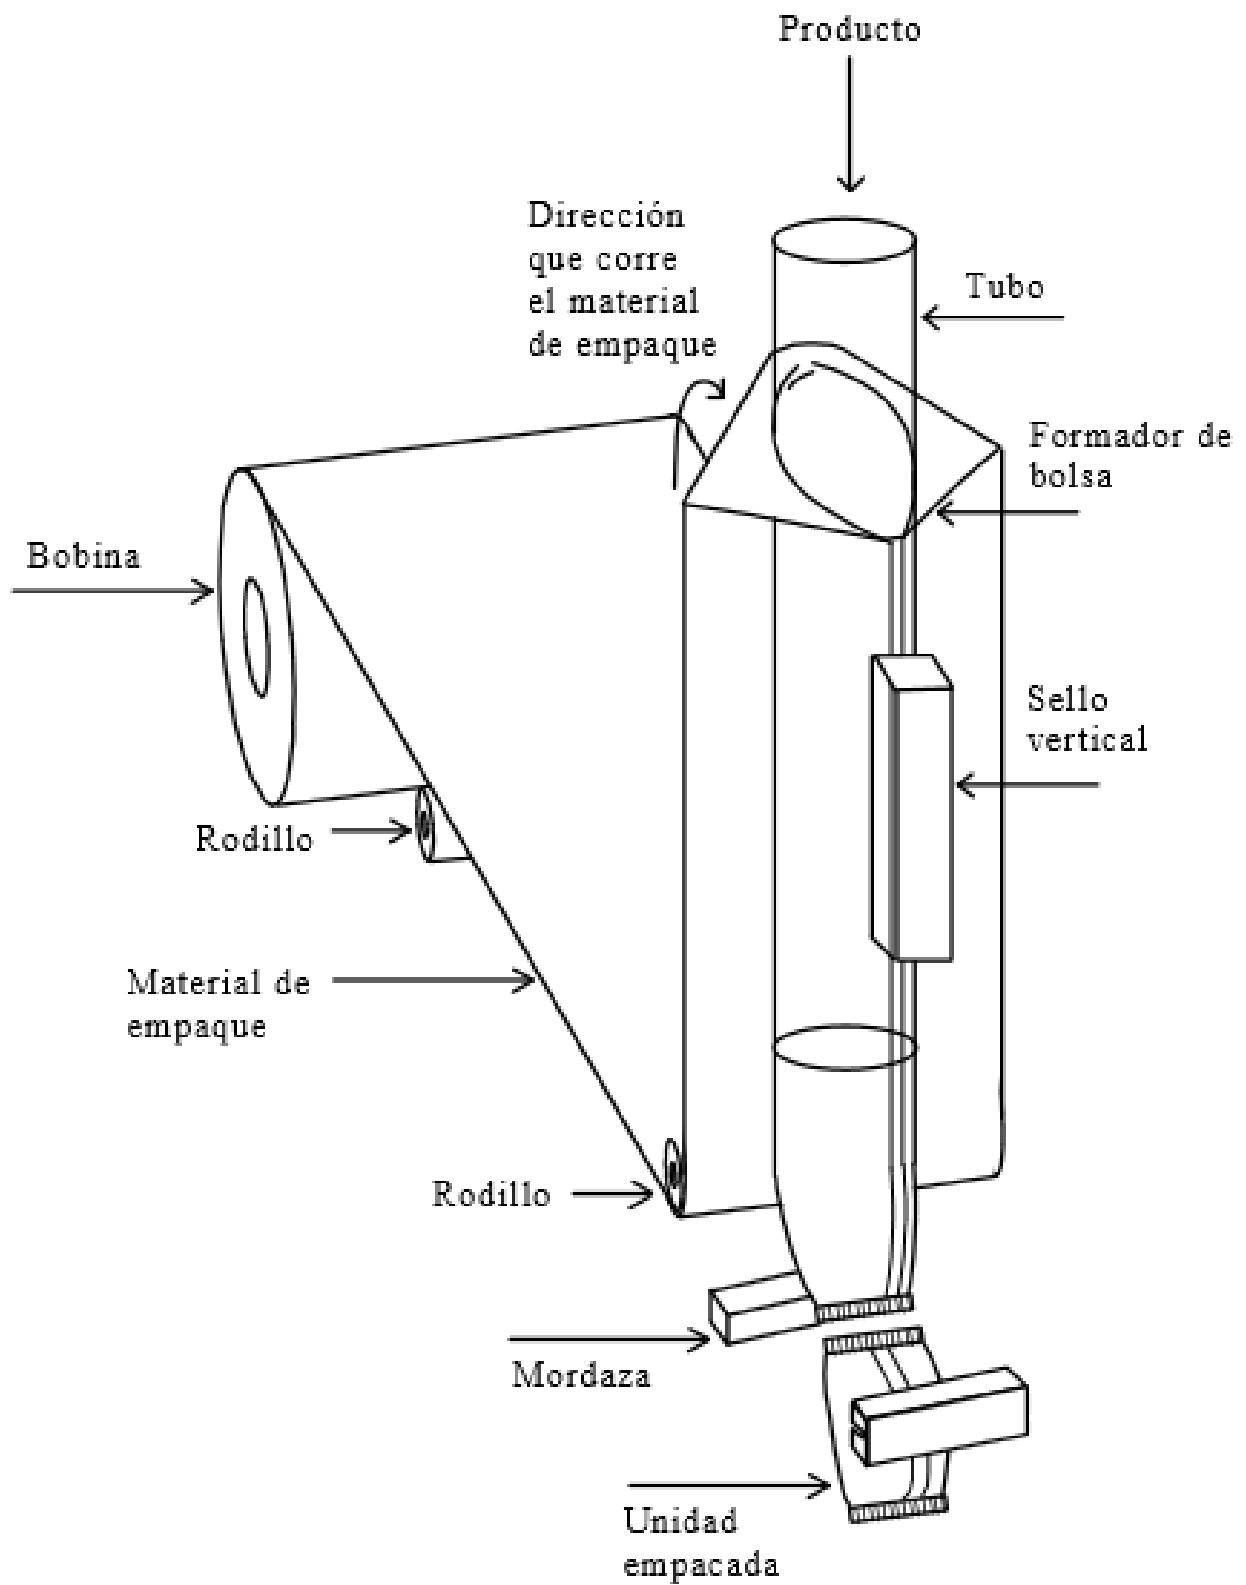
Conjunto formador del empaque(UNAD, s.f.).
